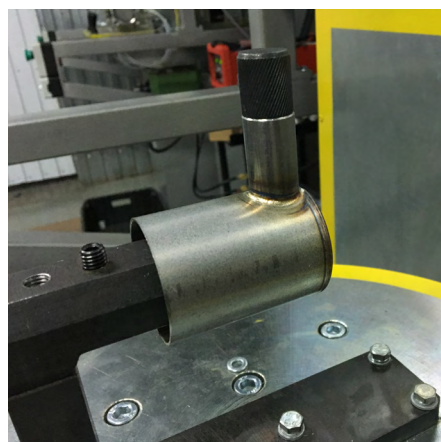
Сідлоподібний шов з'єднання бонки з корпусом, зварений на АС 399-С3
